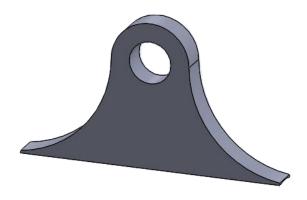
Diseño final de la lengüeta Fuente: Elaboración Propia
